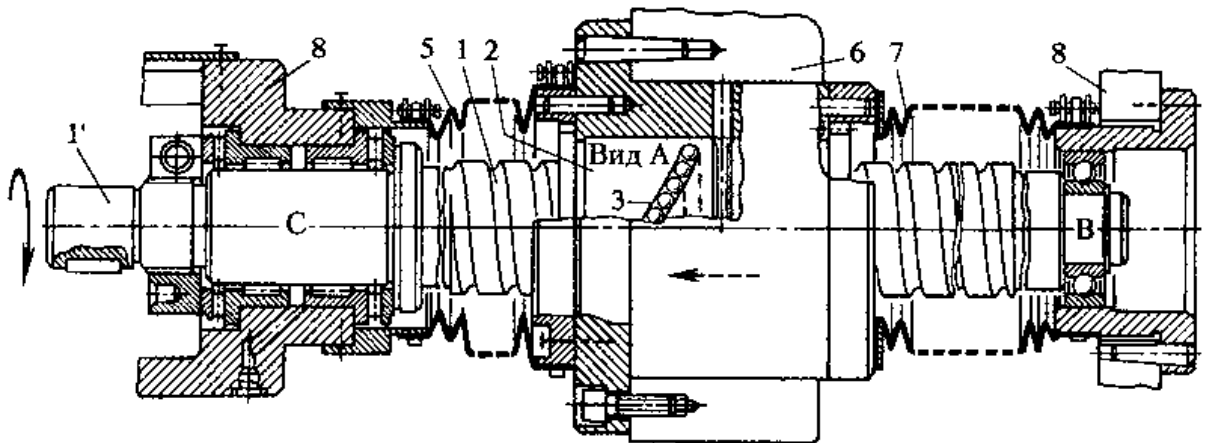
Конструктивное решение использования ШВП в механизме подачи станка
